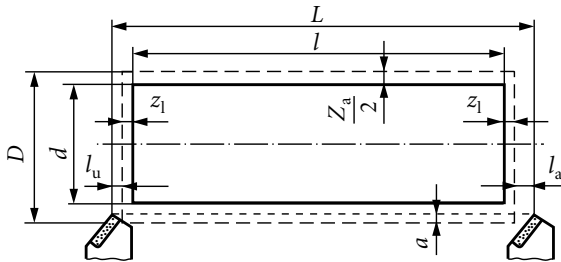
Vorschubweg und Bearbeitungszugaben am Drehteil
